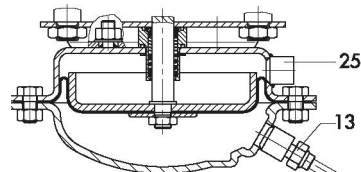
универсальный редуктор давления тип 41-23, показан в разрезе
